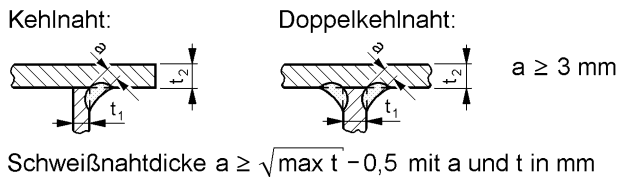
Schweißnahtdicke a von Kehlnähten
